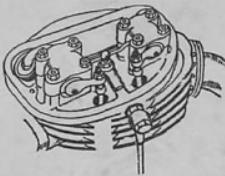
Головка цилиндра двигателя ЭСО с коромыслами и толкателями.
